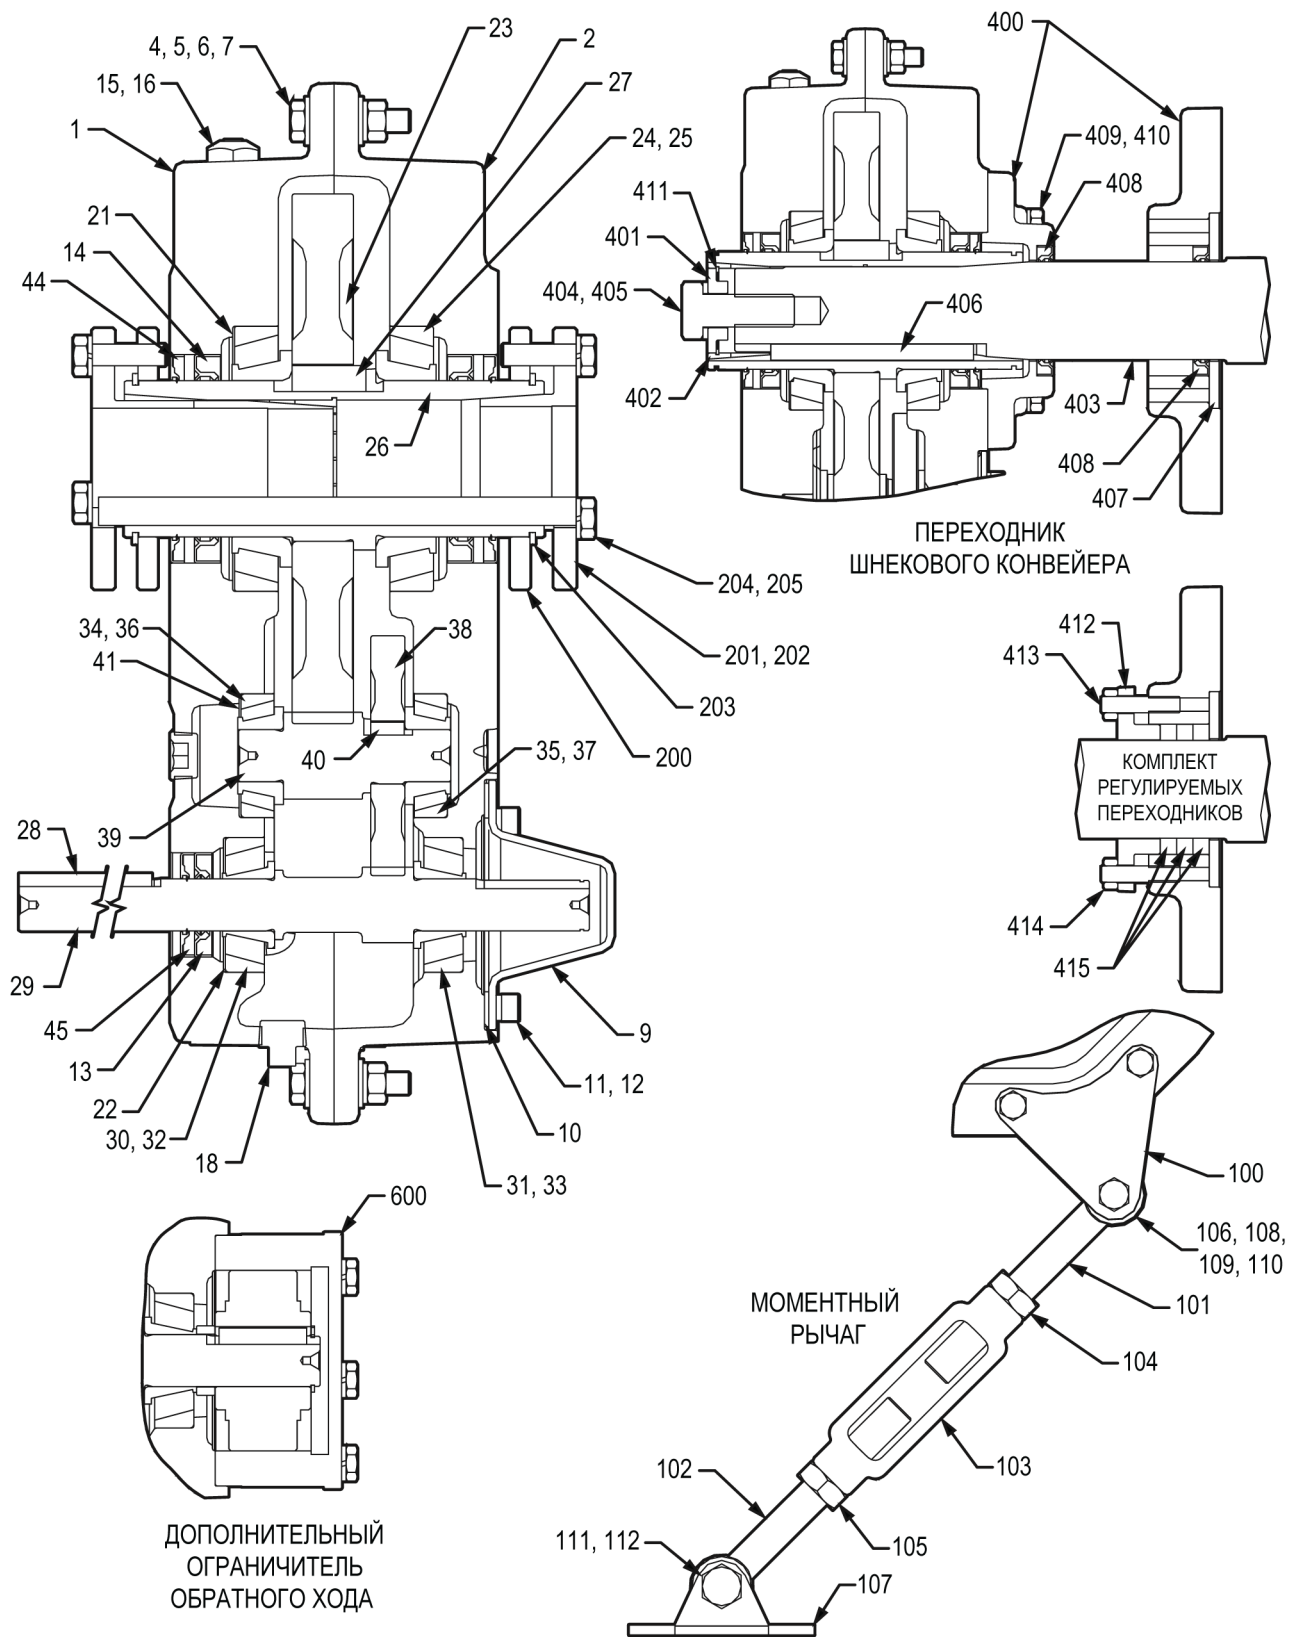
Детали для двухступенчатых редукторов с коническими втулками ТА0107L-ТА12608Н
